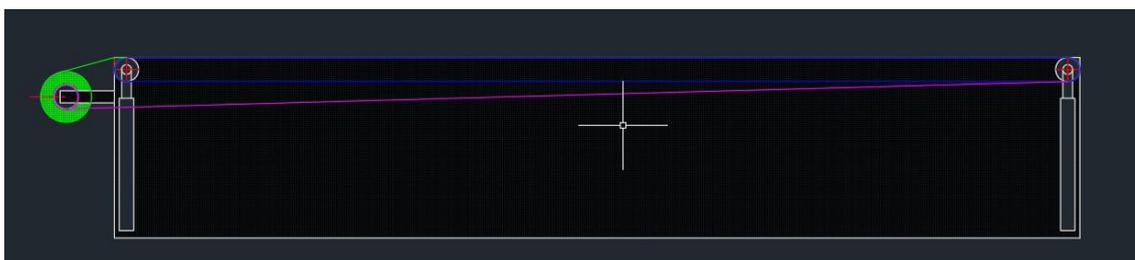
Sistema eje-cable con lona enrollada y cilindros bajados.
